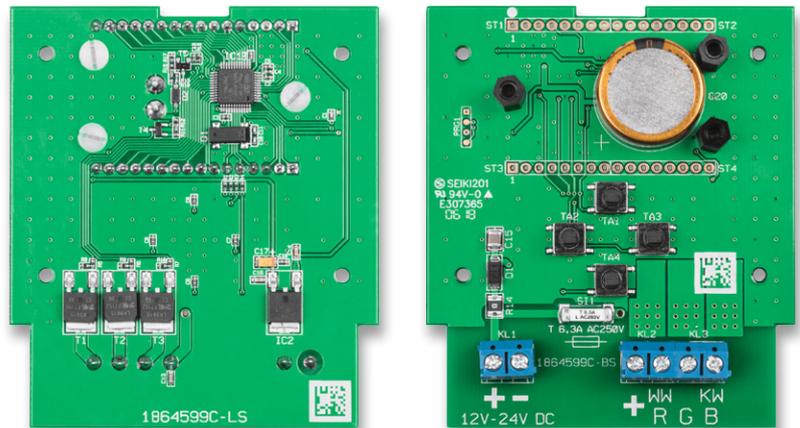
Die mit Schraubklemmen, Goldcap und Abstandhaltern bestückte Platine. Links sieht man die von unten eingesetzten Kunststoffschrauben.
